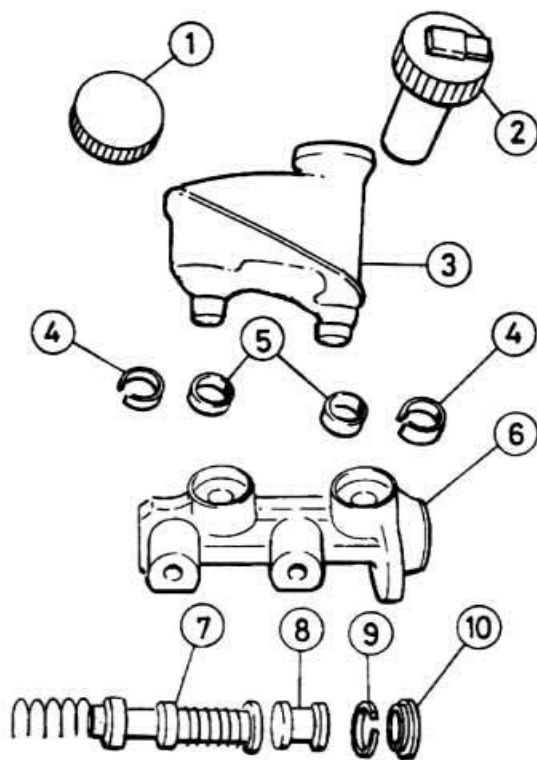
Главный тормозной цилиндр типа GMF в разобранном виде:
